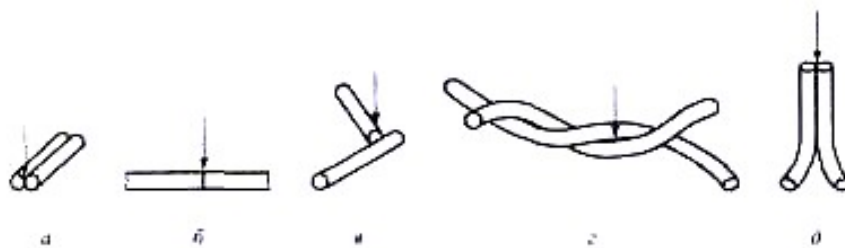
Типы сварных соединений проволоки:
